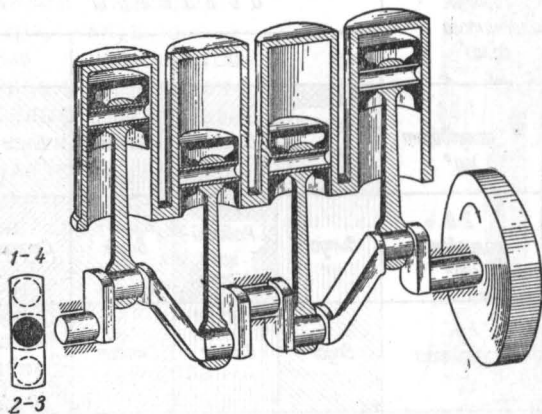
Рабочий процесс четырехтактного четырехцилиндрового карбюраторного двигателя
